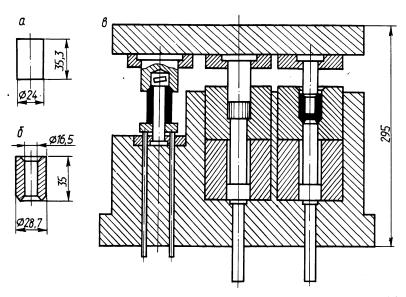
Заготовка (а), поковка детали (б) и штамп для ее выдавливания (в)
